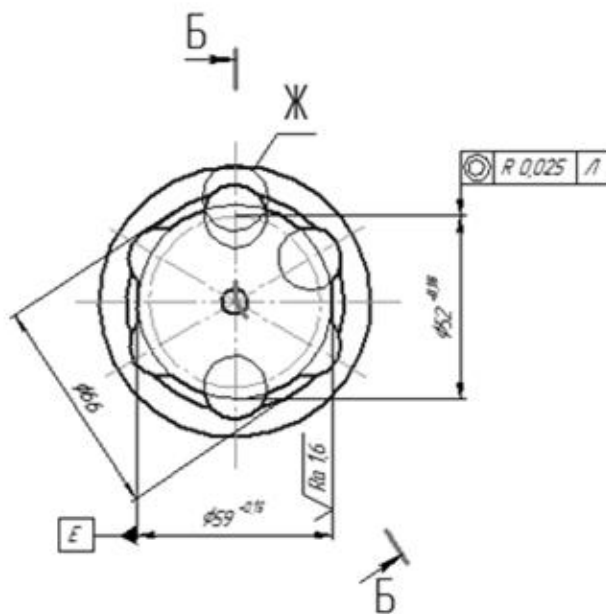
Чертеж детали корпус внутреннего шарнира автомобиля LADA Granta
